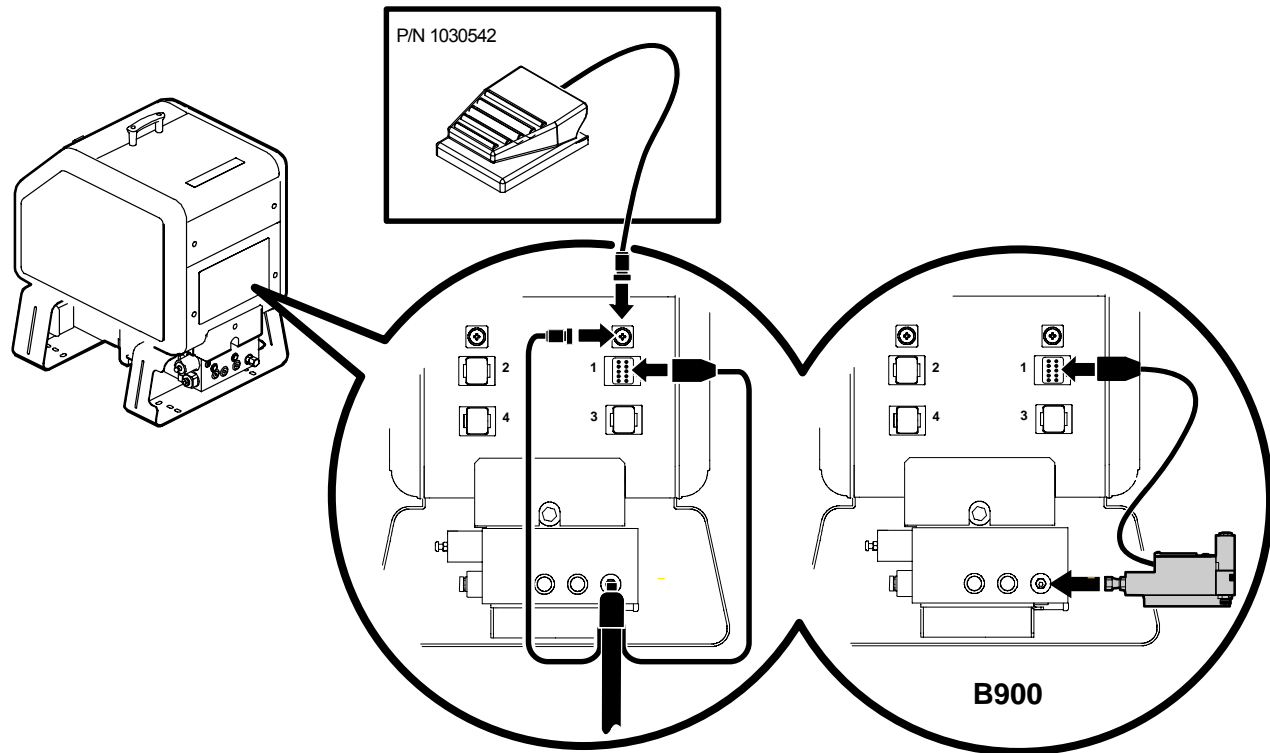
Schlauch für Handpistole mit Schalter oder Fußschalter anschließen
